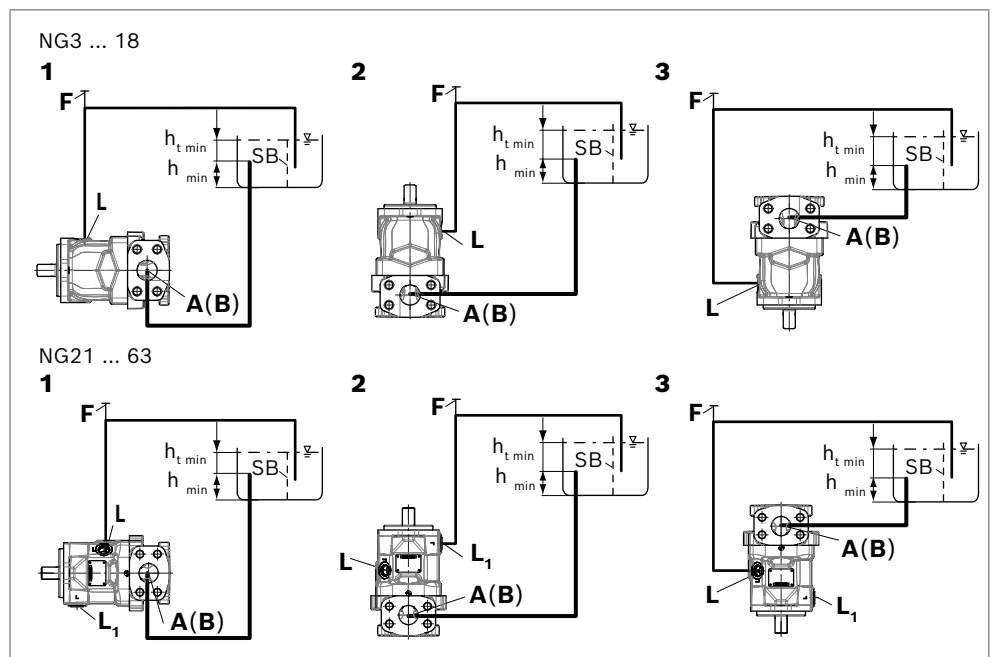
Untertankeinbau A10FZO mit Einbaulage 1-3
